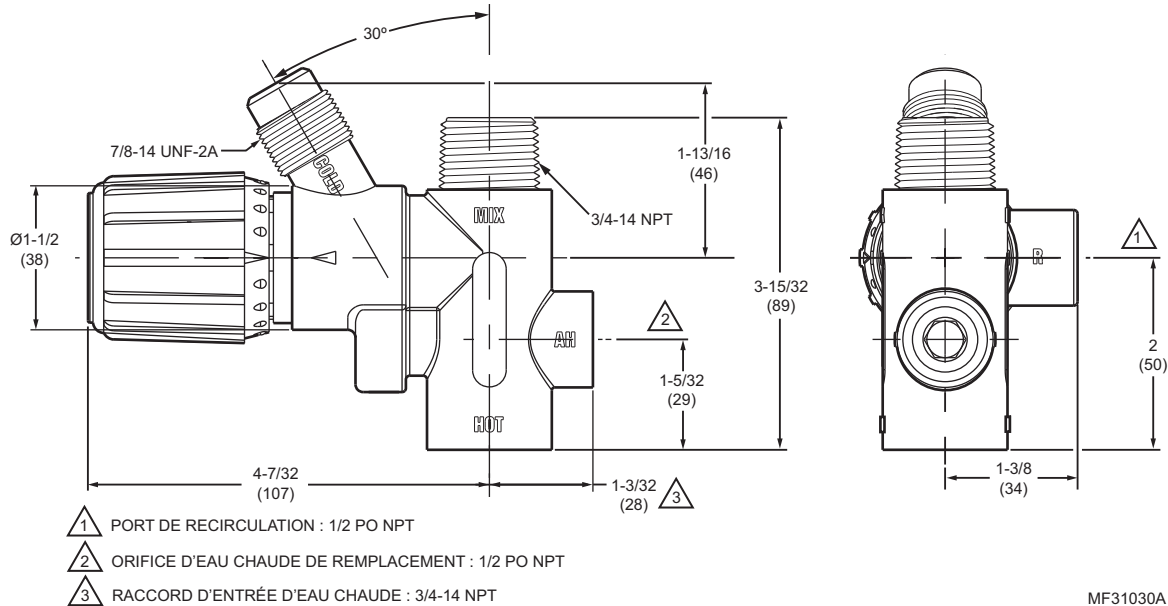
Dimensions de la vanne de mélange AMX300 en po (mm).
